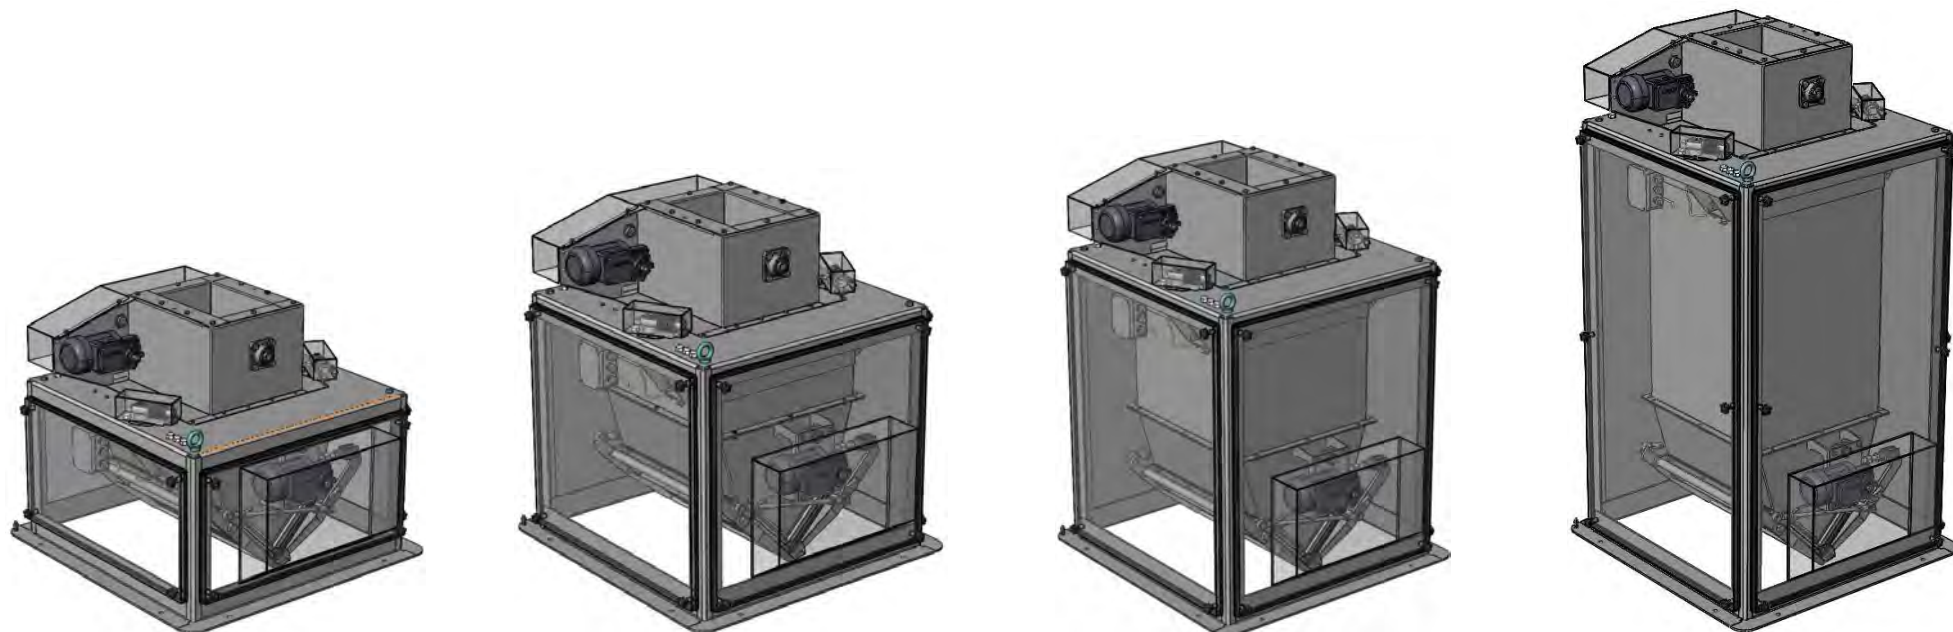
Весы «Поток» исполнения АВБ с пневматическими приводами. Габаритно-установочные размеры.
